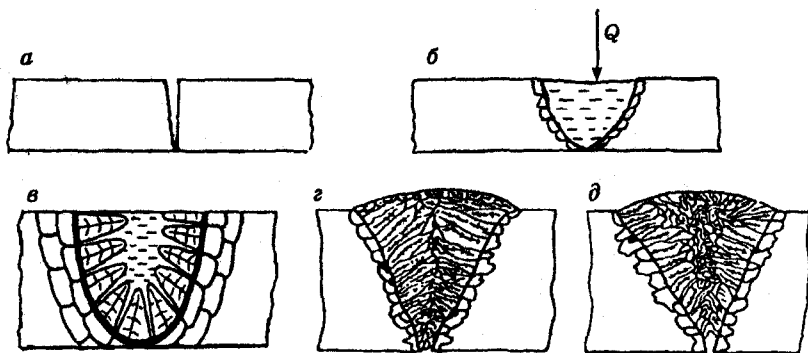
Схема образования сварного соединения при сварке плавлением:
